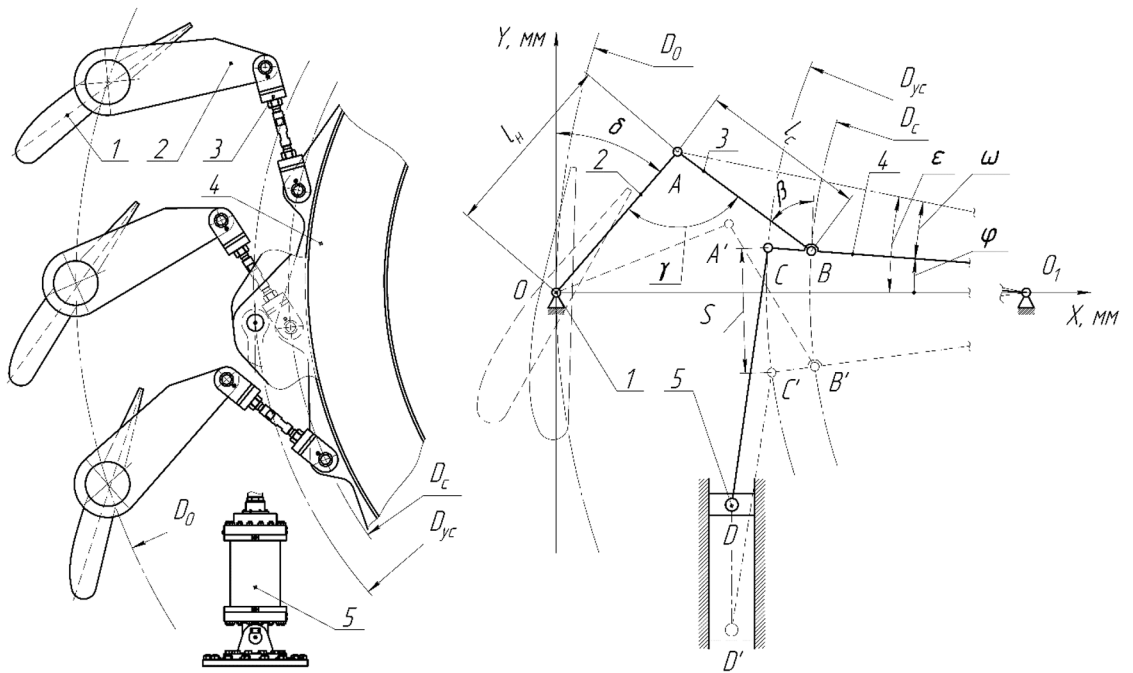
Схематизация направляющего аппарата: 1 — лопатка направляющего аппарата; 2 — накладка; 3 — серьга; 4 — регулирующее кольцо; 5 — сервомотор
